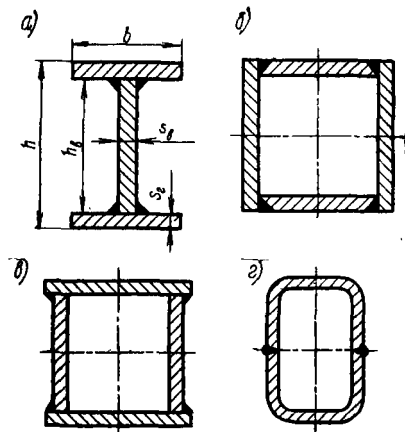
Типы поперечных сечений сварных балок:
